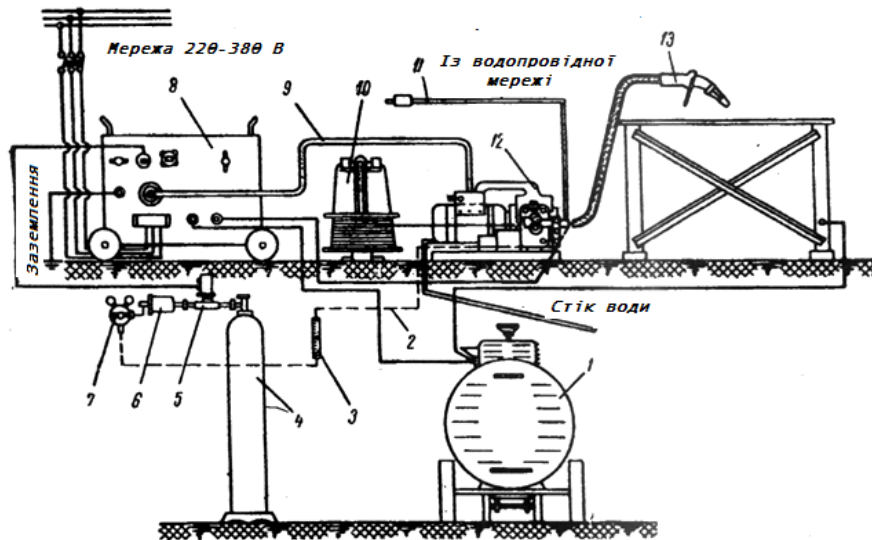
Схема установки для напівавтоматичного зварювання в середовищі вуглекислого газу
